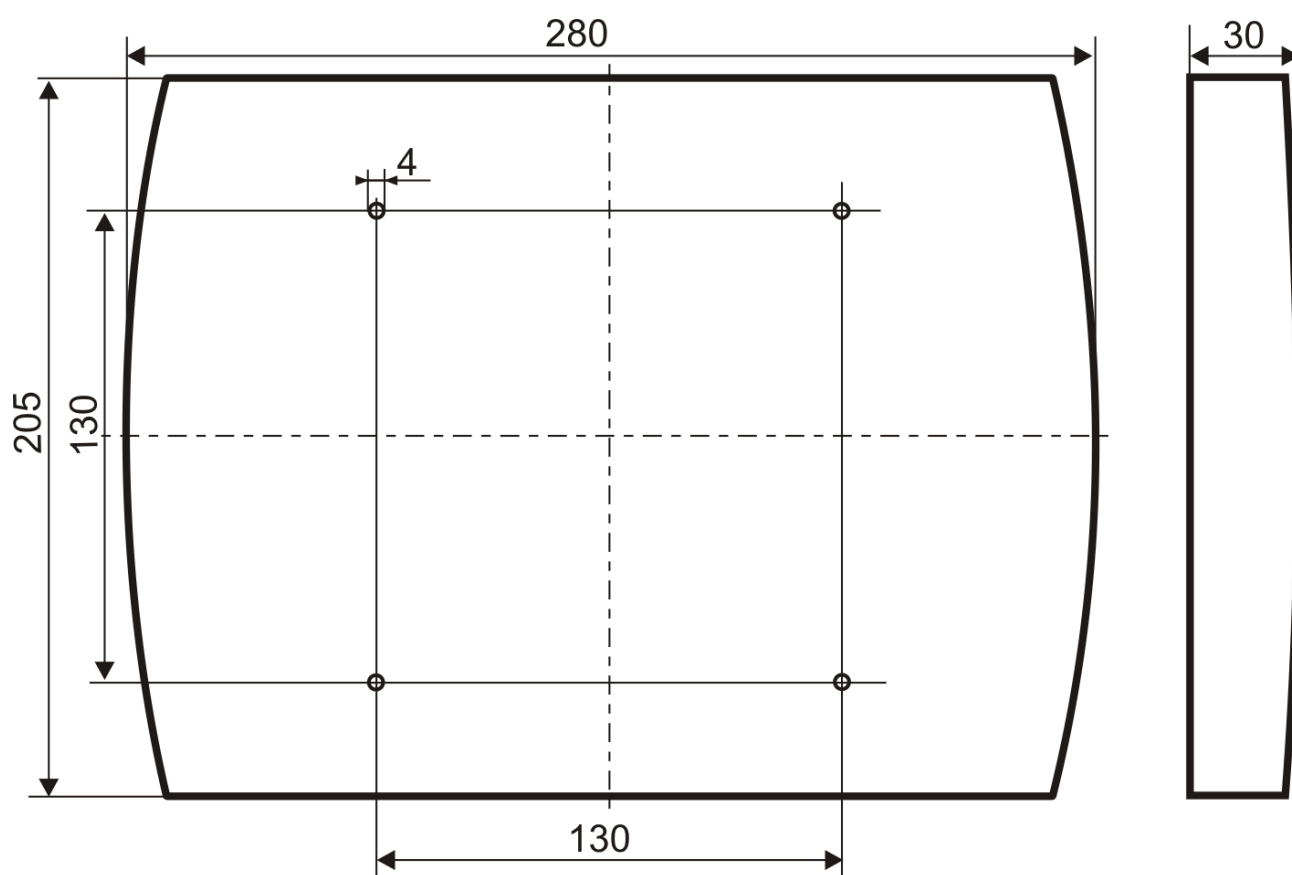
Габаритные и установочные размеры SF-DC3232
